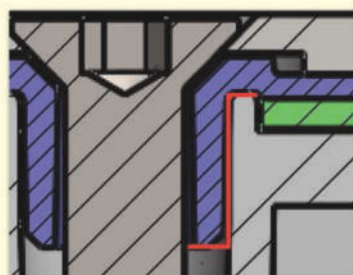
Поперечний переріз зі шляхами струмів витоку від кріпильного гвинта до PCB
